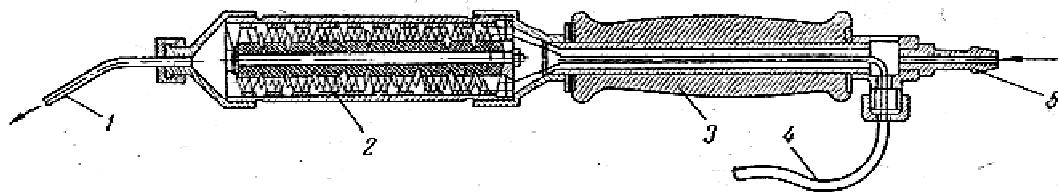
Пистолет для сварки полиэтилена и винипласта:
